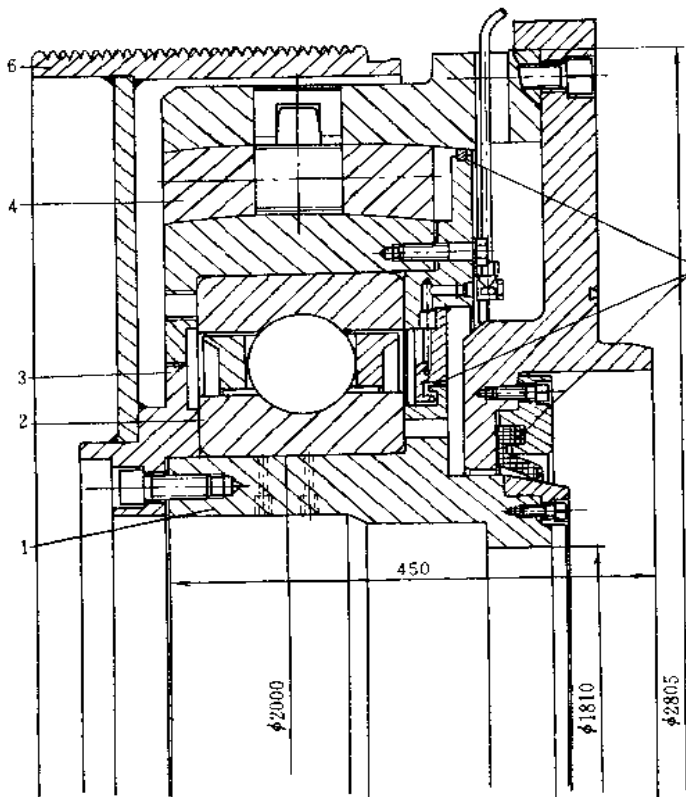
深沟球轴承和三环滑动球轴承的新型组合轴承
